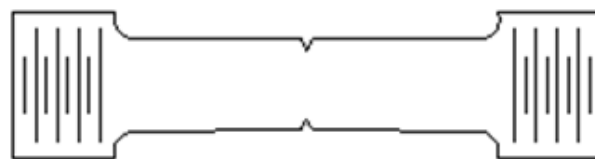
Цилиндрический образец с кольцевым надрезом для испытания на растяжение
